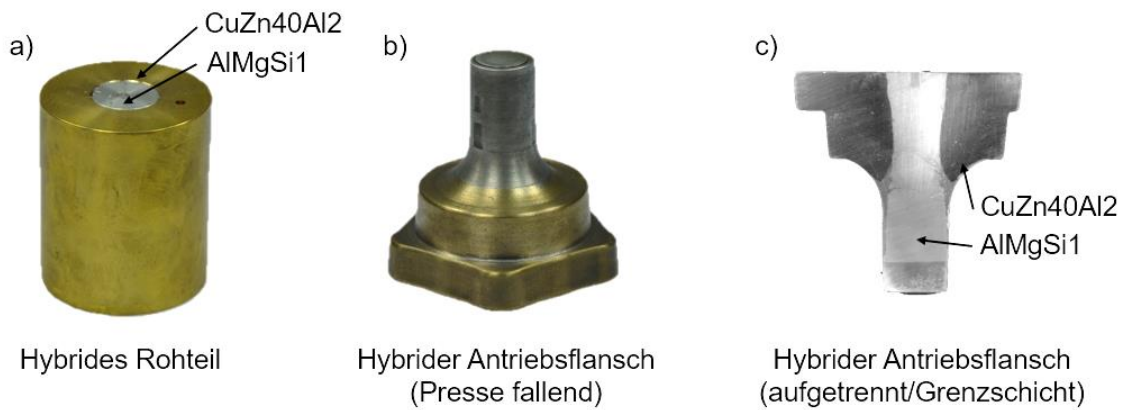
Messing-Aluminium-Verbundbauteil; a) Hybrid raw part; b) Hybrid drive flange (hot pressed); c) Hybrid drive flange (sectioned/interfacial layer)
